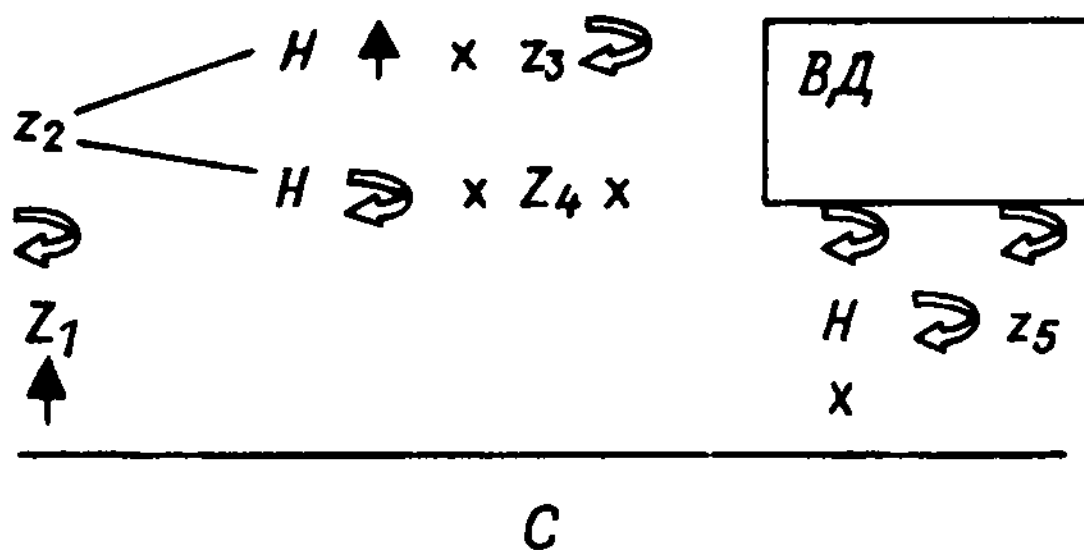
Структурная схема станка для закалки шеек коленчатого вала:
